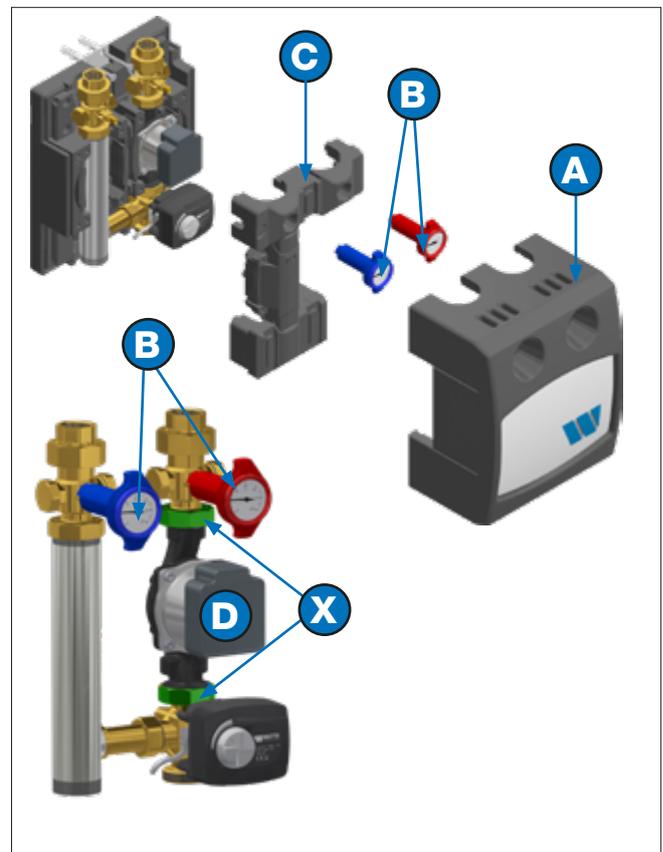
Smontaggio e assemblaggio della pompa di circolazione
